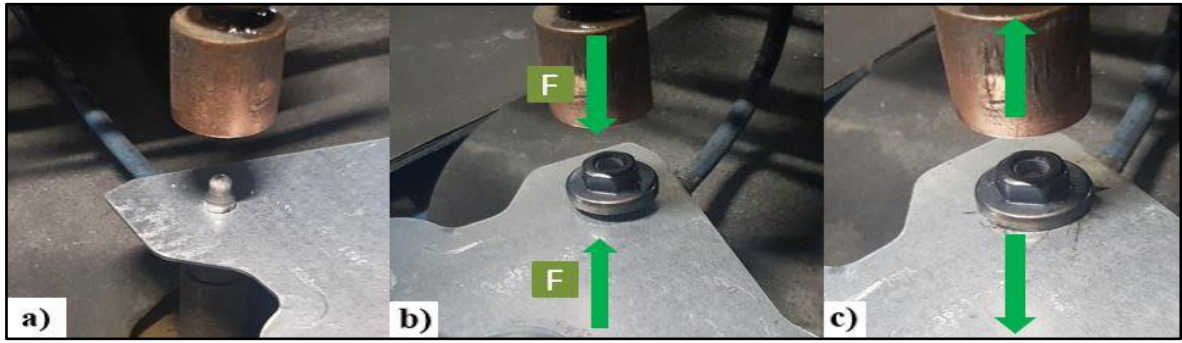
a) Tecna weld tester, b) Akım doğrulama c) Kuvvet doğrulama görseli.
